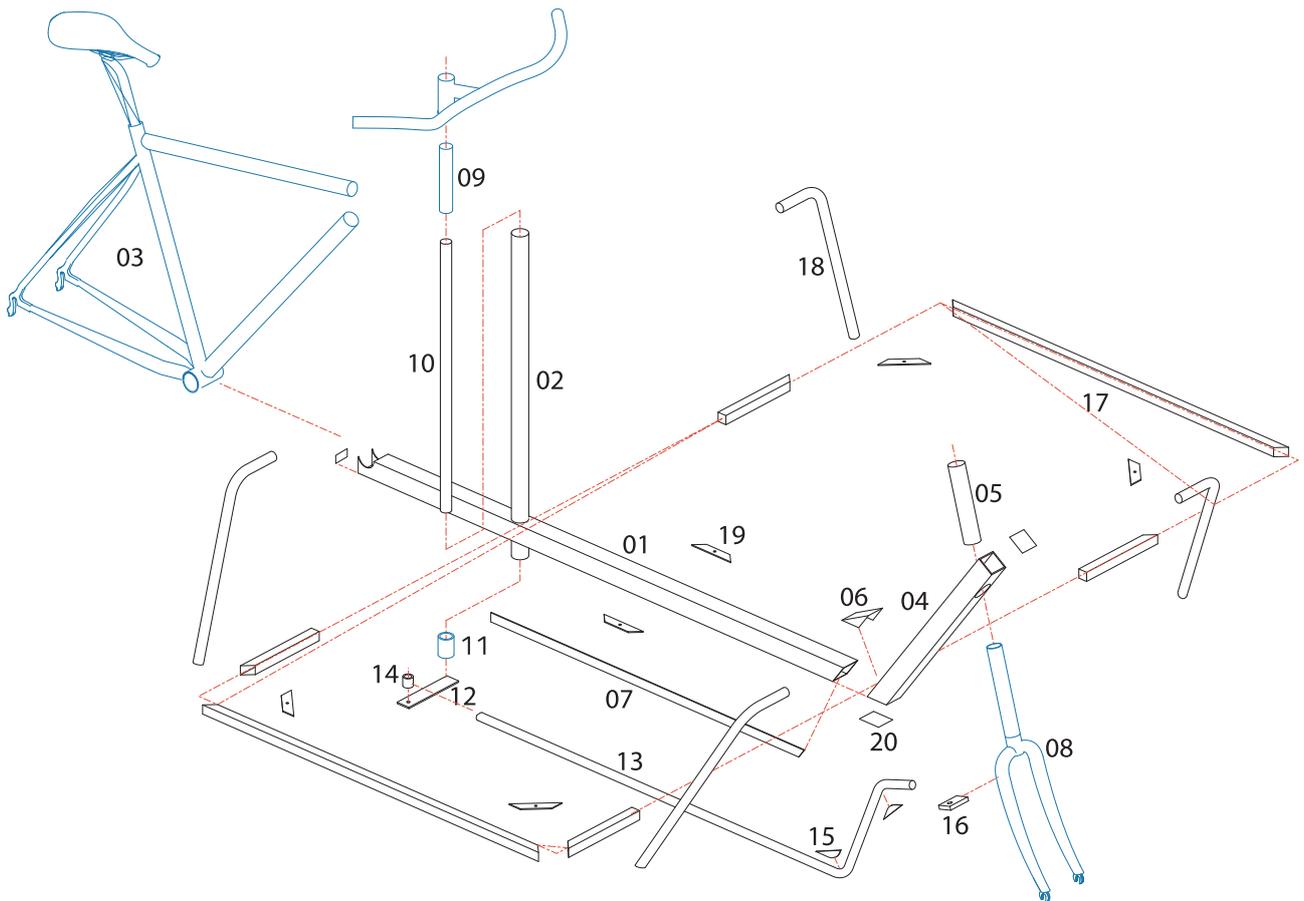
Explosionsskizze des Lastenrades; Quelle: [1]
